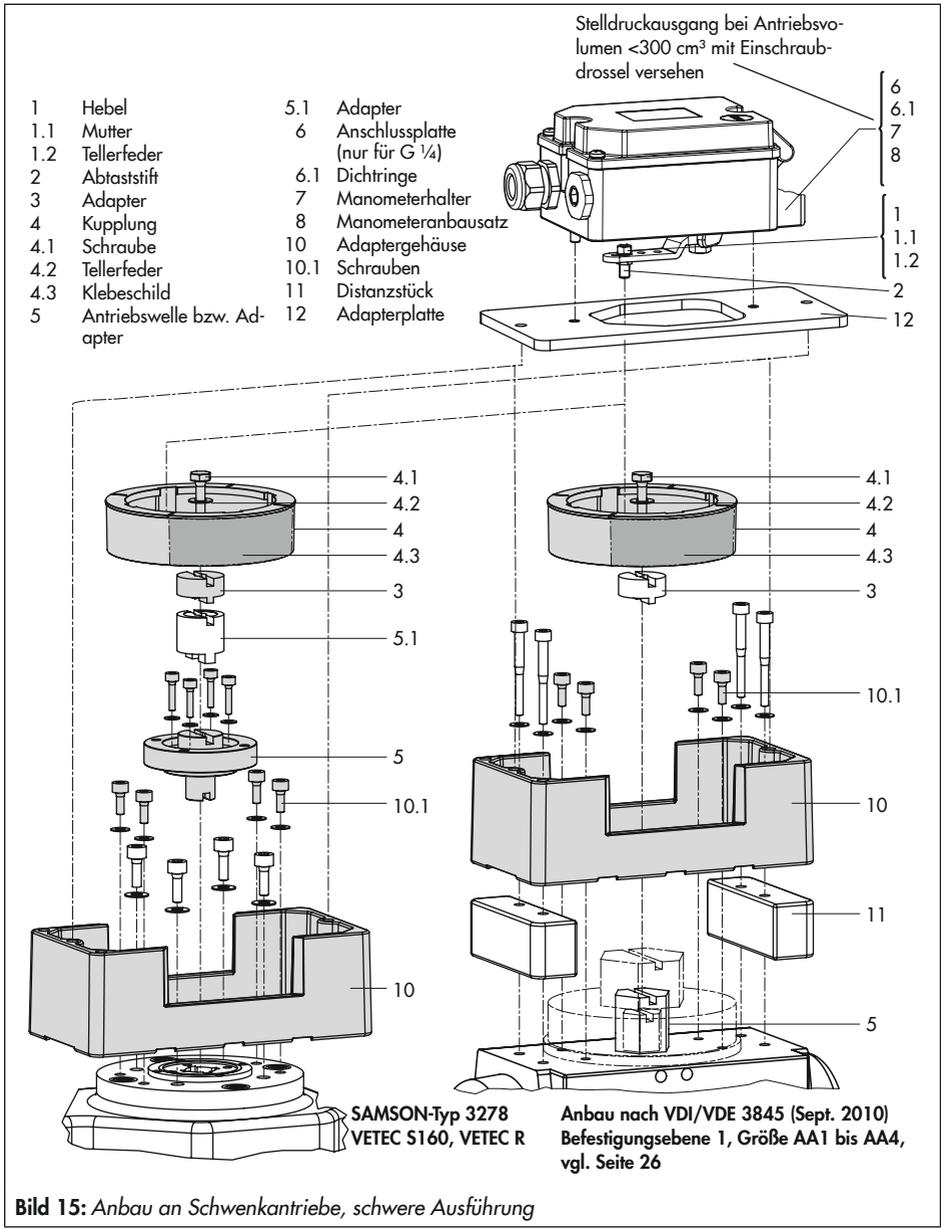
Anbau an Schwenkantriebe, schwere Ausführung
